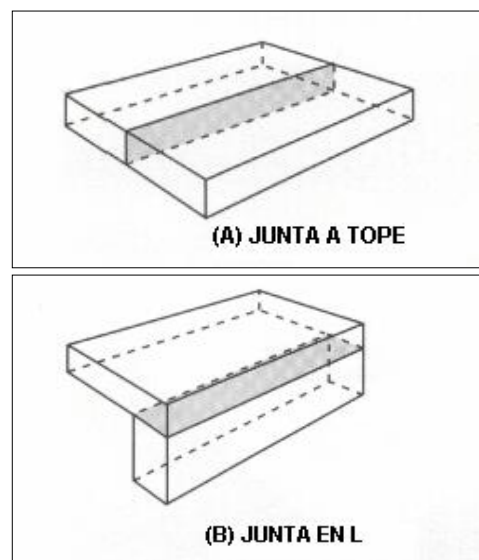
TIPOS DE JUNTA PARA SOLDAR
